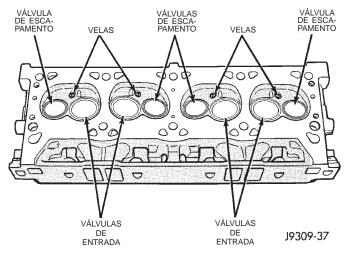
Conjunto do Cabeçote de Cilindros PISTÕES
